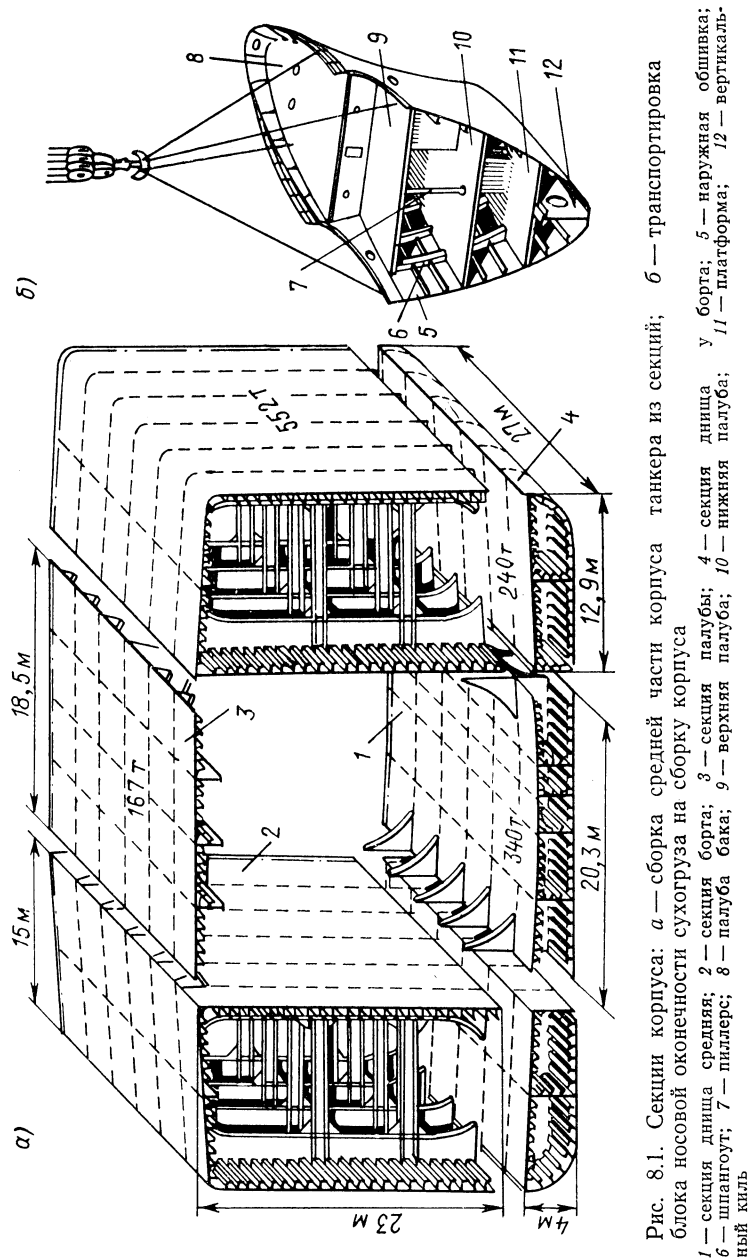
Секции корпуса: а — сборка средней части корпуса танкера из секций; б — транспортировка блока носовой оконечности сухогруза на сборку корпуса
